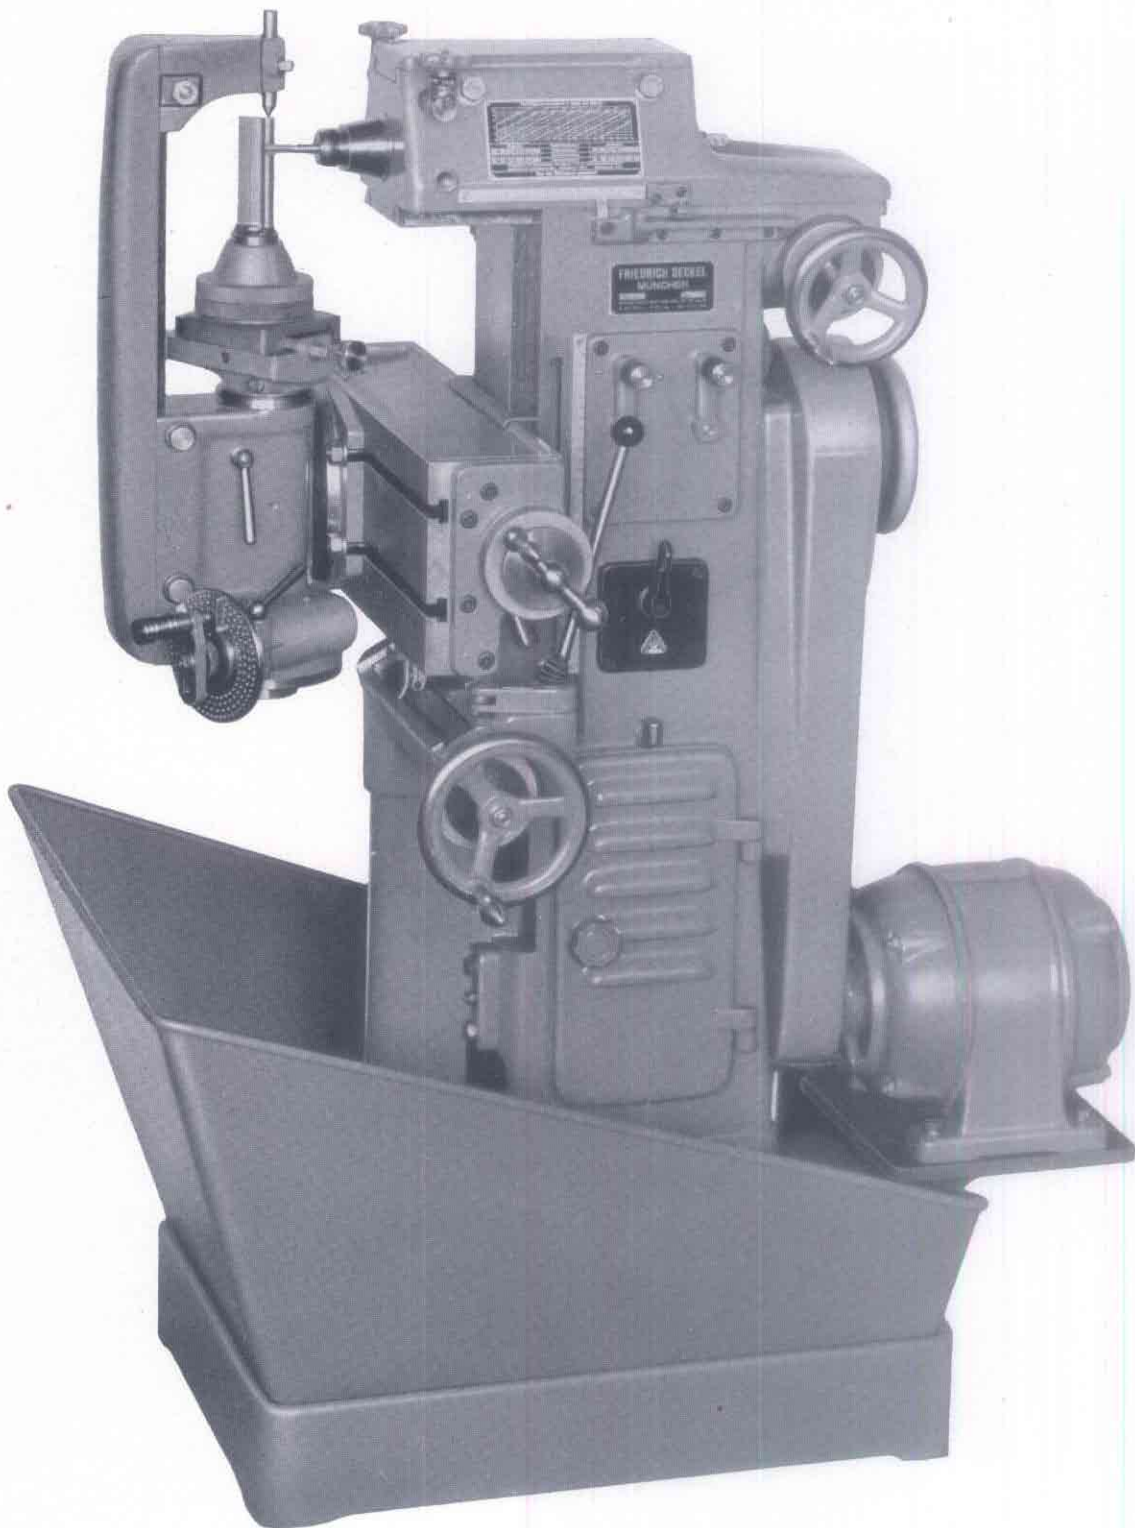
FP 1 Maschine eingerichtet für das Stempelfräsen
